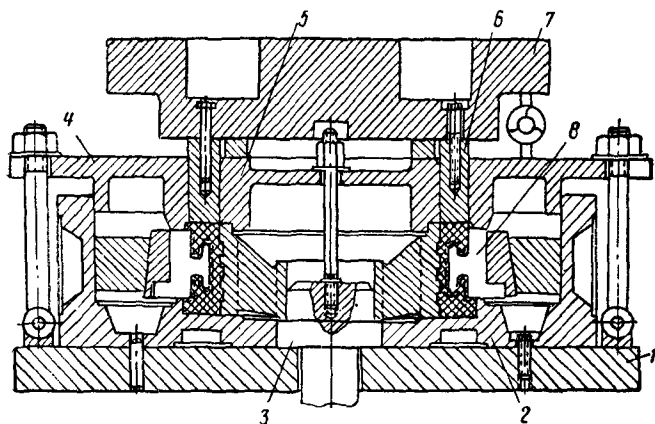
Прессформа для изготовления коллекторов с пластмассовым корпусом:
